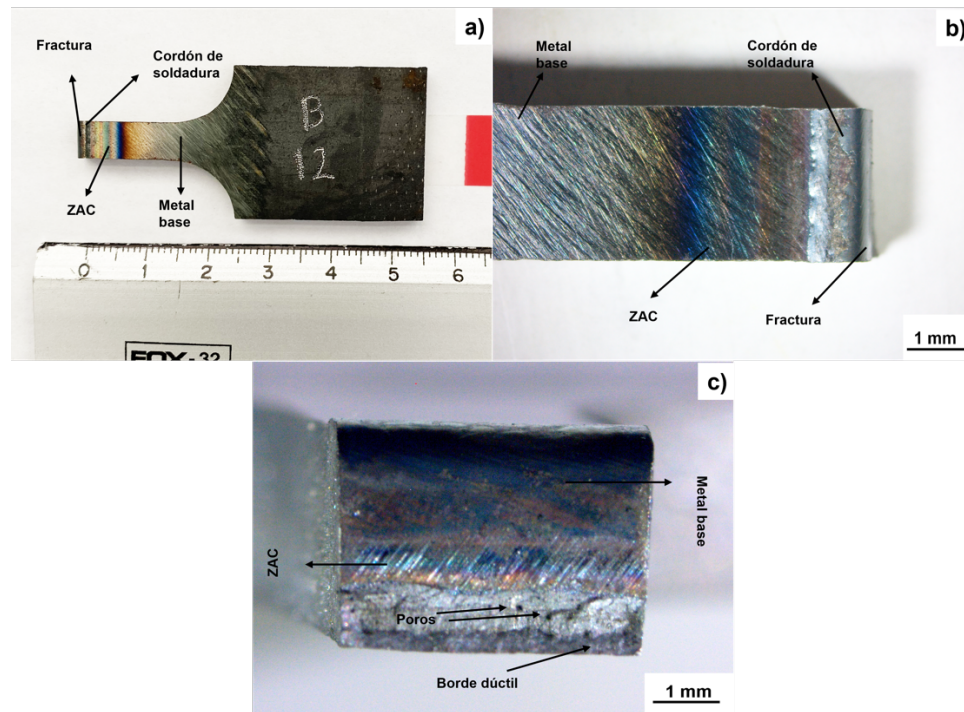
Fractografía para unión GTAW12B donde a) vista macroscópica con fractura en la soldadura, b) vista longitudinal de la zona del cordón a la fractura, c) toma transversal del cordón donde se observa falta de penetración.
